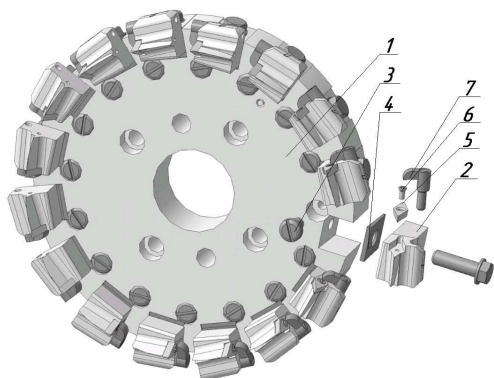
Двухсторонняя торцовая резцовая головка со сборными резцами
